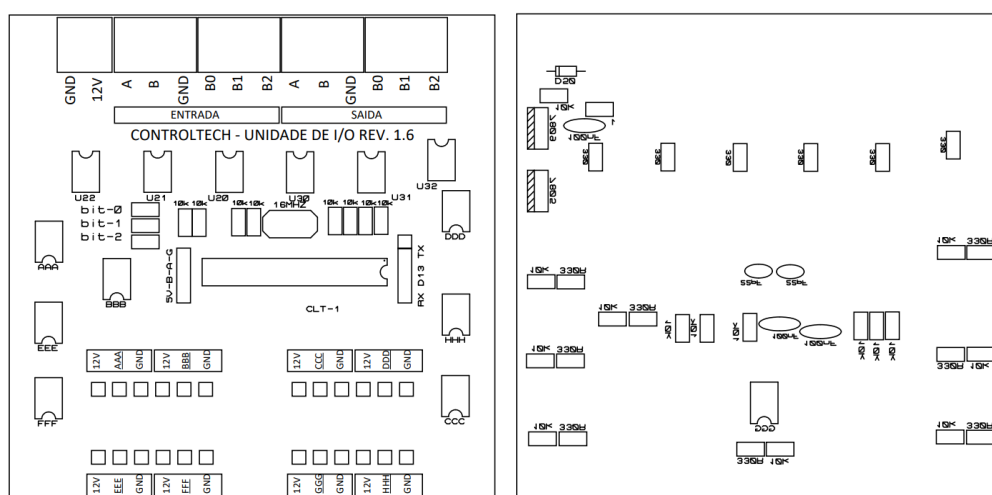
Vista superior e inferior PCB I/O Ver. 1.6
